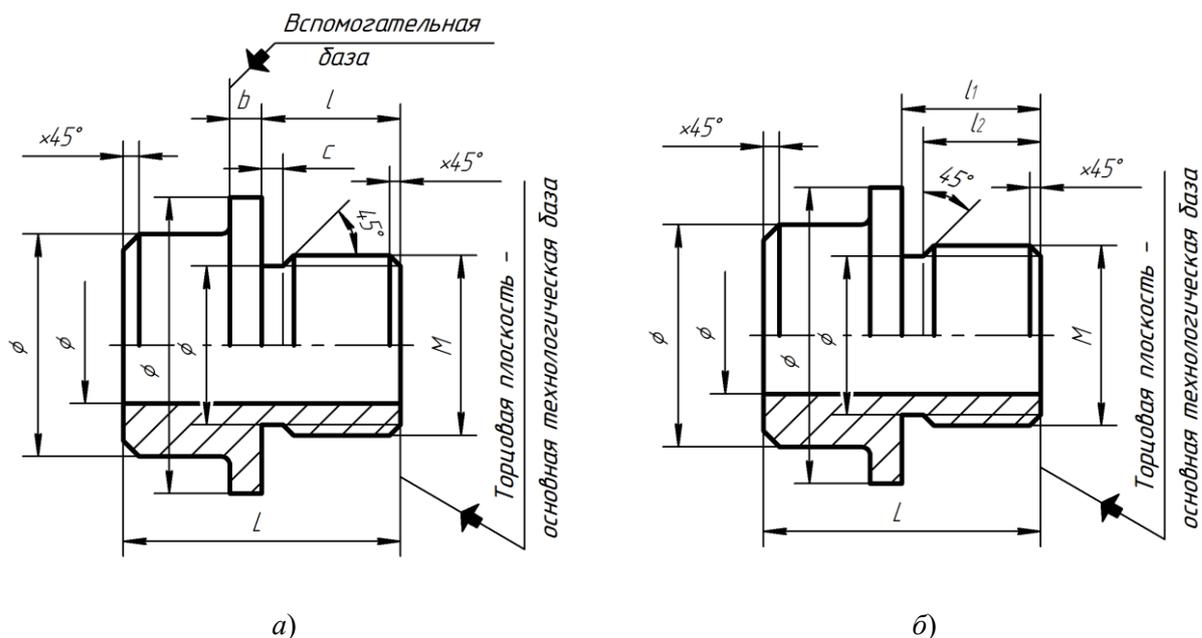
Варианты простановки размеров на чертеже штанцера:
